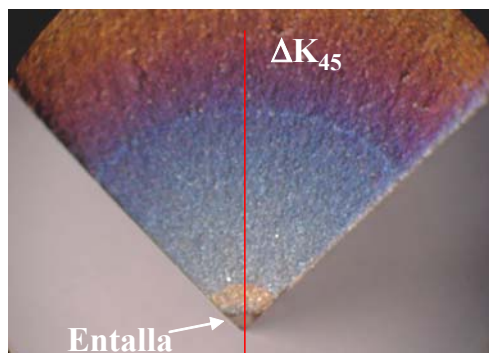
Geometría de la grieta Corner Crack, CC (6,5X)
